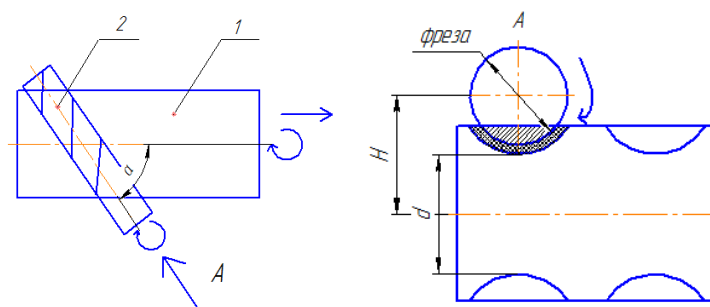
Схема обработки шнека: 1 – заготовка; 2 – концевая фреза
